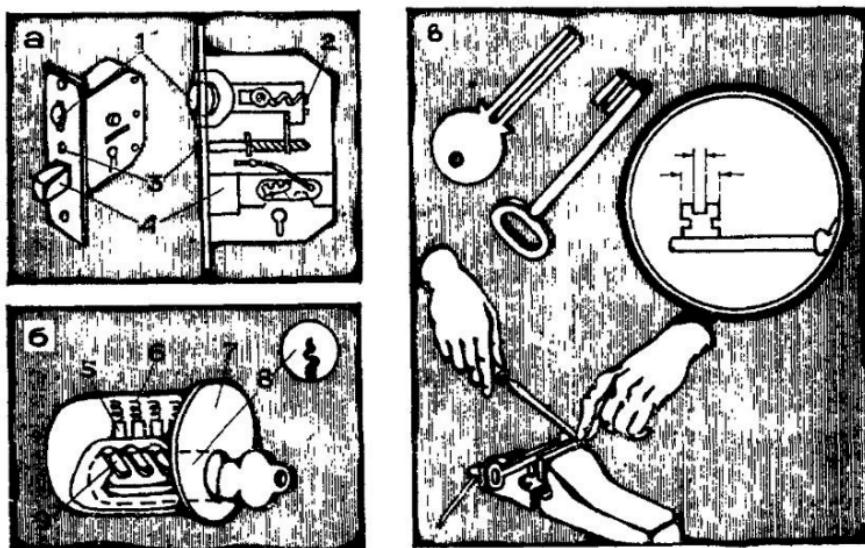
Устройство врезных (а), с цилиндровым механизмом (б)
